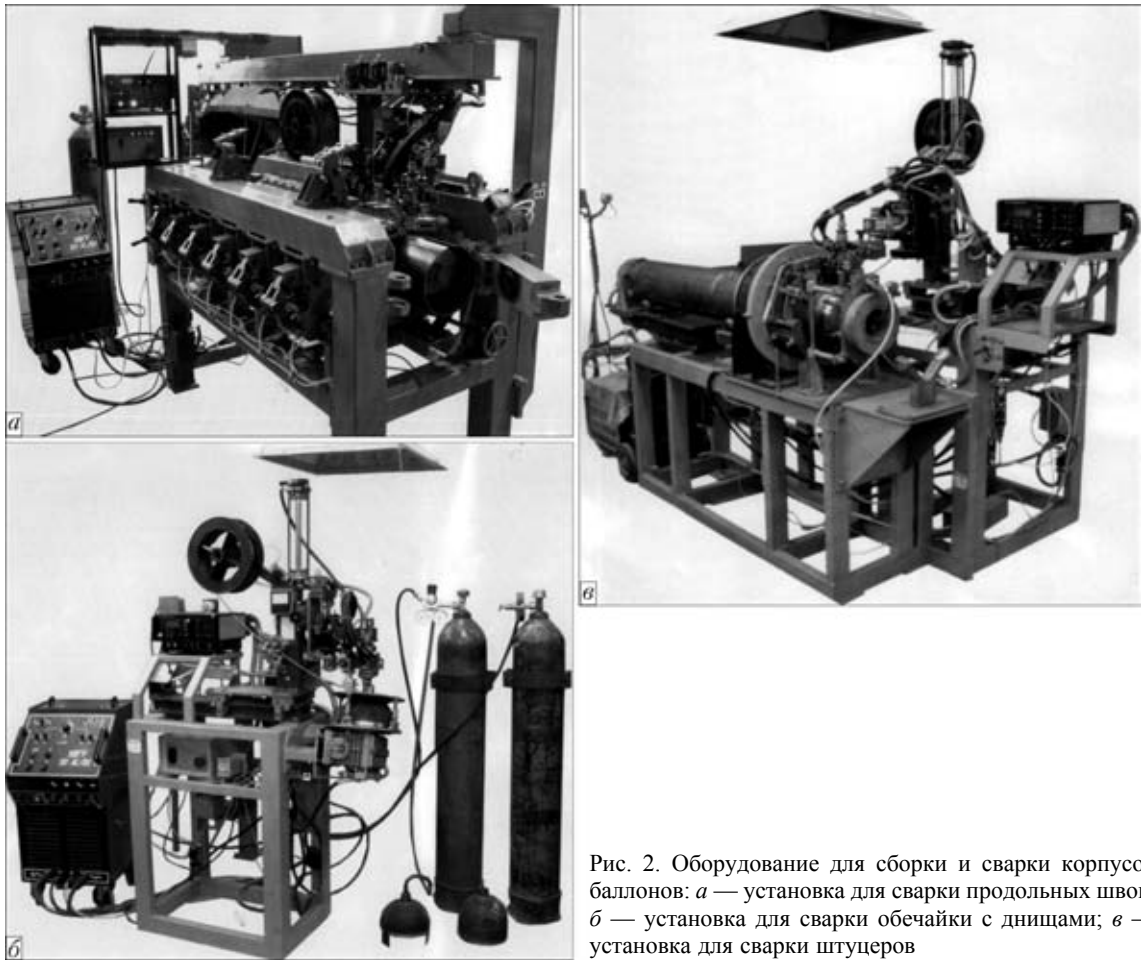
Оборудование для сборки и сварки корпусов баллонов: *а* — установка для сварки продольных швов; *б* — установка для сварки обечайки с днищами; *в* — установка для сварки штуцеров
